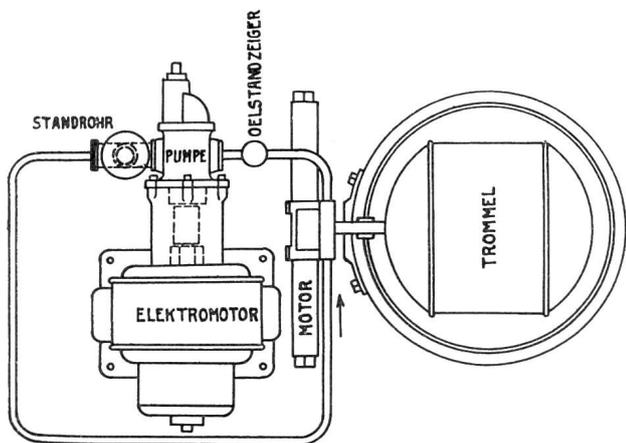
Waschmaschinen-Antrieb, System Egli, Grundriss
